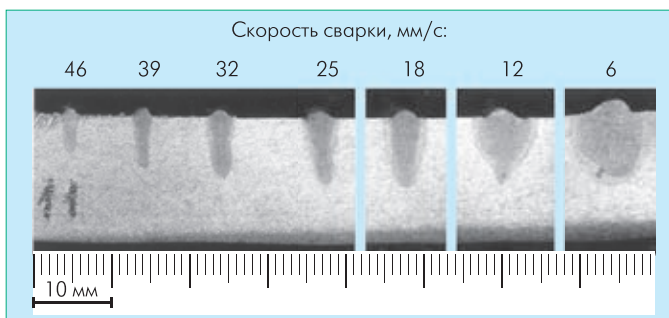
Поперечный макрошлиф из коррозионностойкой стали 08Х18Н10Т. Сварка выполнялась на цилиндрическом образце, в гелии, "на подъем"
